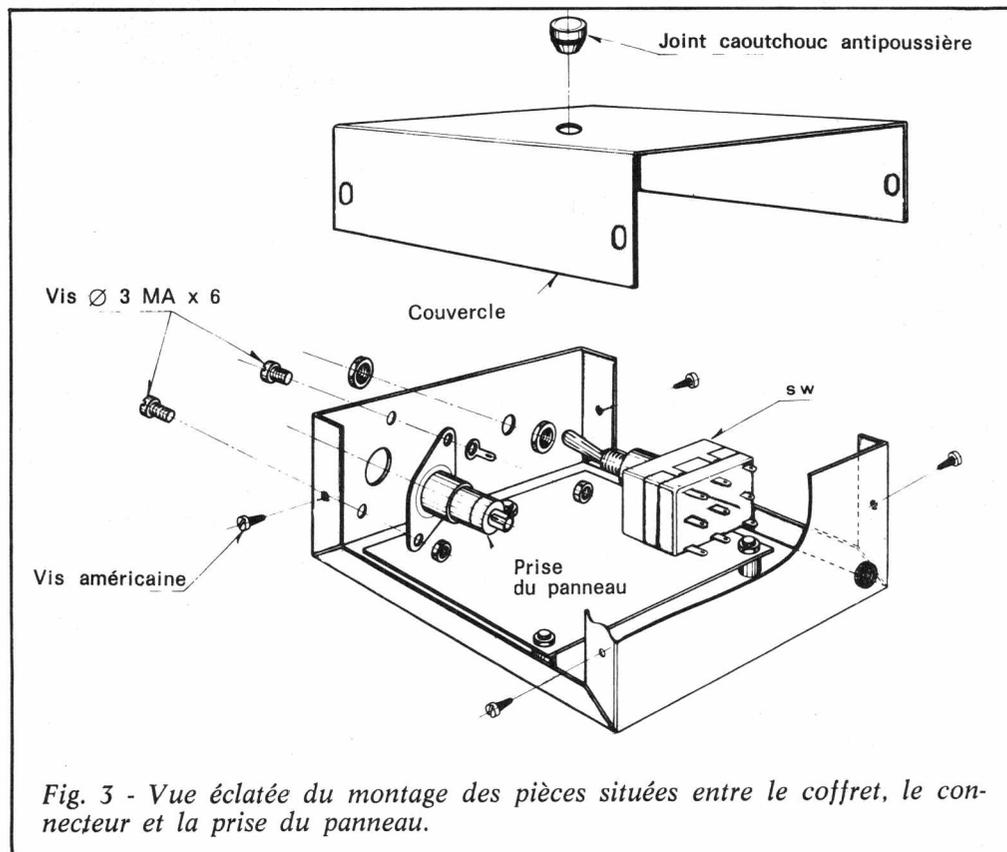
Vue éclatée du montage des pièces situées entre le coffret, le connecteur et la prise du panneau.
